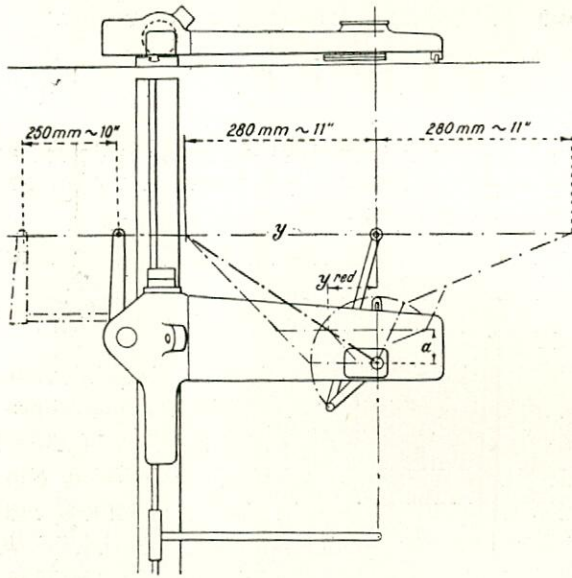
Alzado y planta del gran integrador Amsler de bola.
